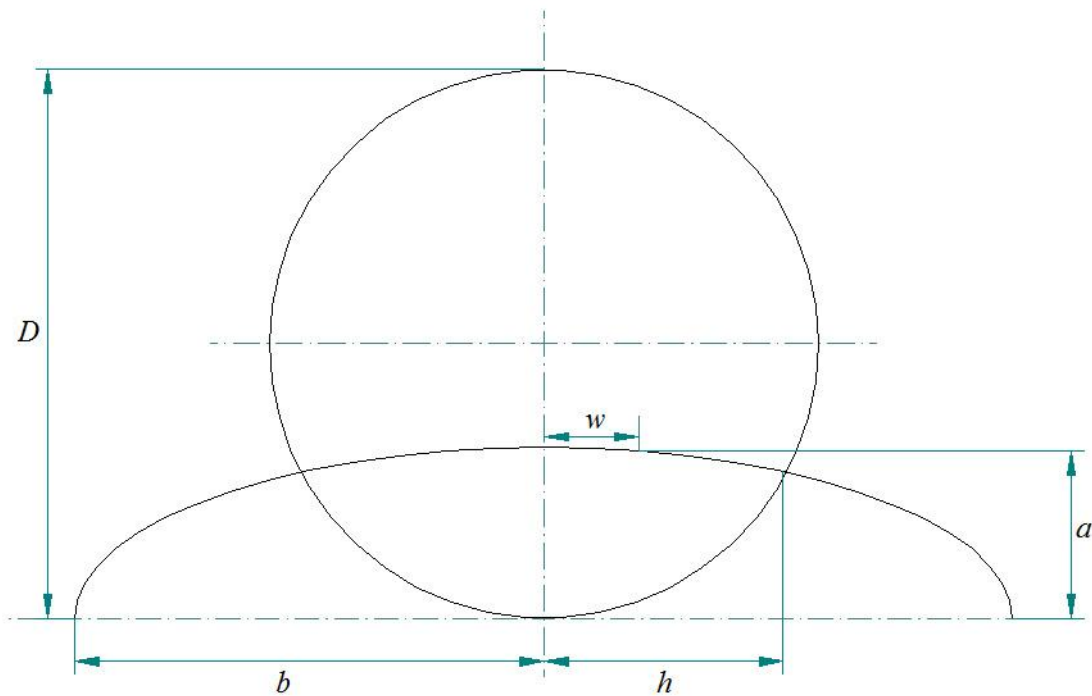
Sección transversal del eje y geometría de la fisura.
